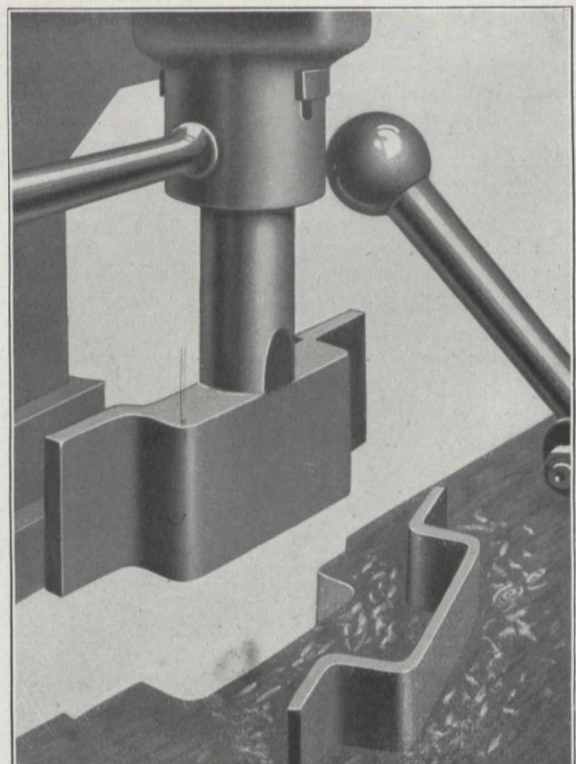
Stemmisen, mit dem heute in kurzer Zeit die Ausschnitte bei den Seitenwänden der R-Wagen maschinell auf das genaueste hergestellt werden, während der Ausschnitt früher von Hand mit der Säge gearbeitet wurde.
